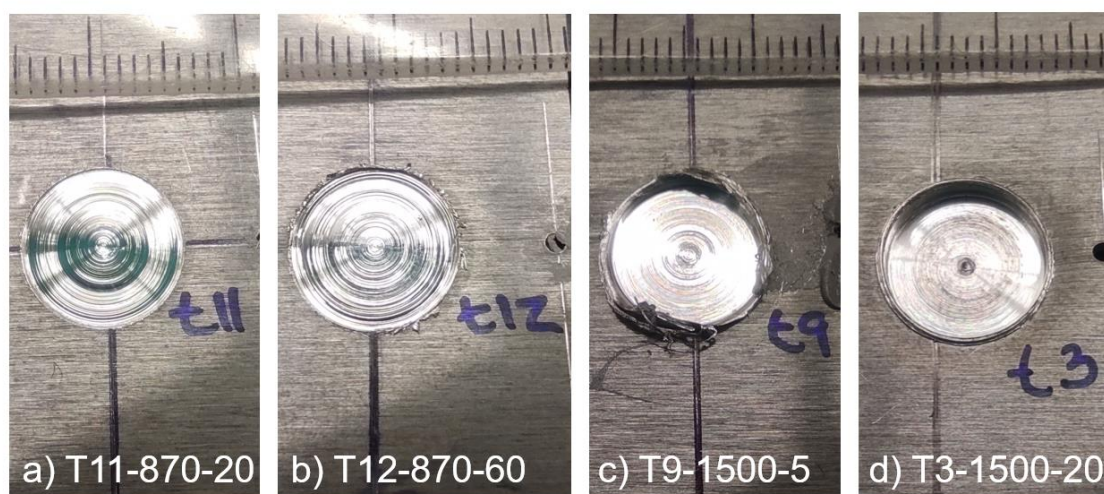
Aspeto visual das soldaduras: a) T11-870-20; b) T12-870-60; c) T9-1500-5; d) T3-1500-20.
